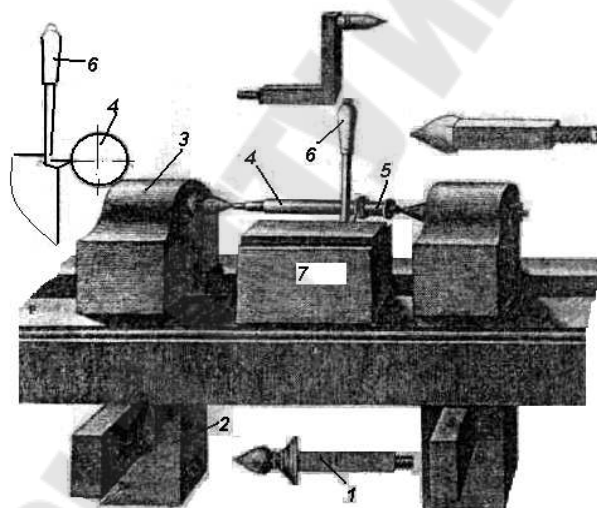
Токарный металлорежущий станок, центра и установка резца. 1701г. по Плюмье
